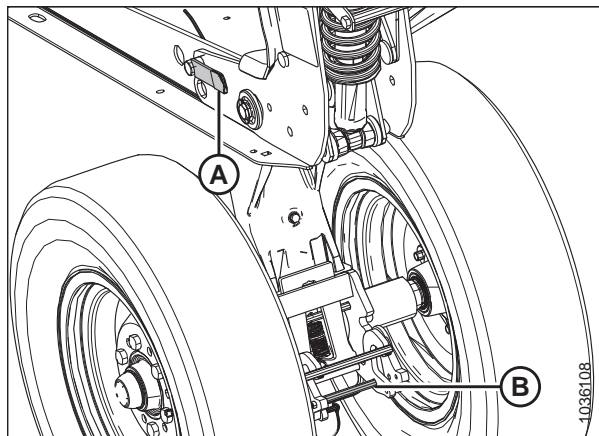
Левые транспортные колеса — шарнир освобожден
